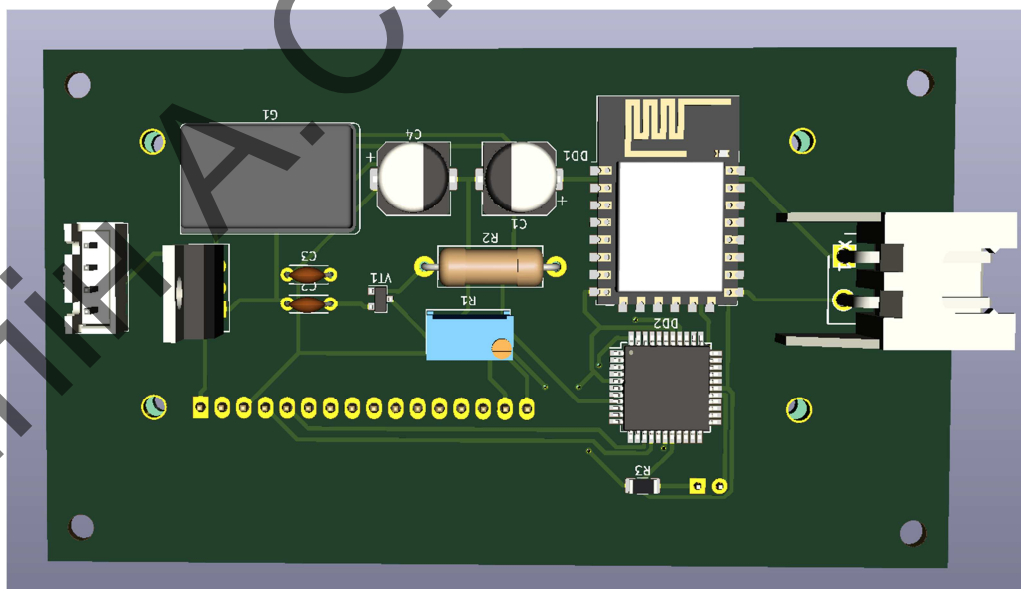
3D модель задньої частини друкованої плати в KiCad
